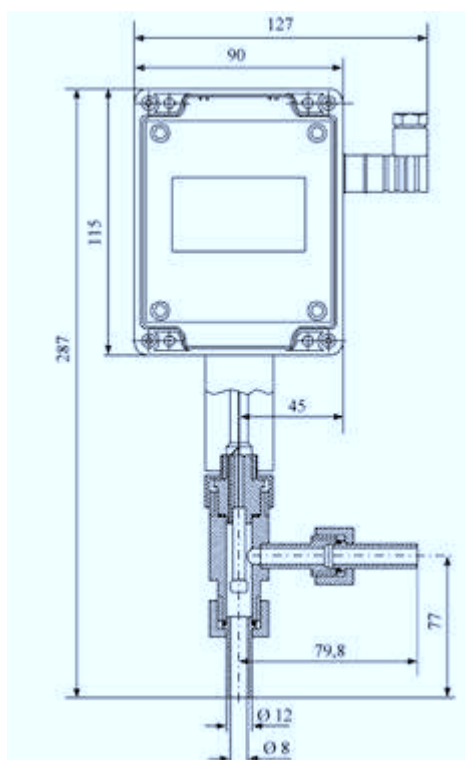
Первичный преобразователь с корпусом из пластмассы, тип "П", проточный, с штуцерами
